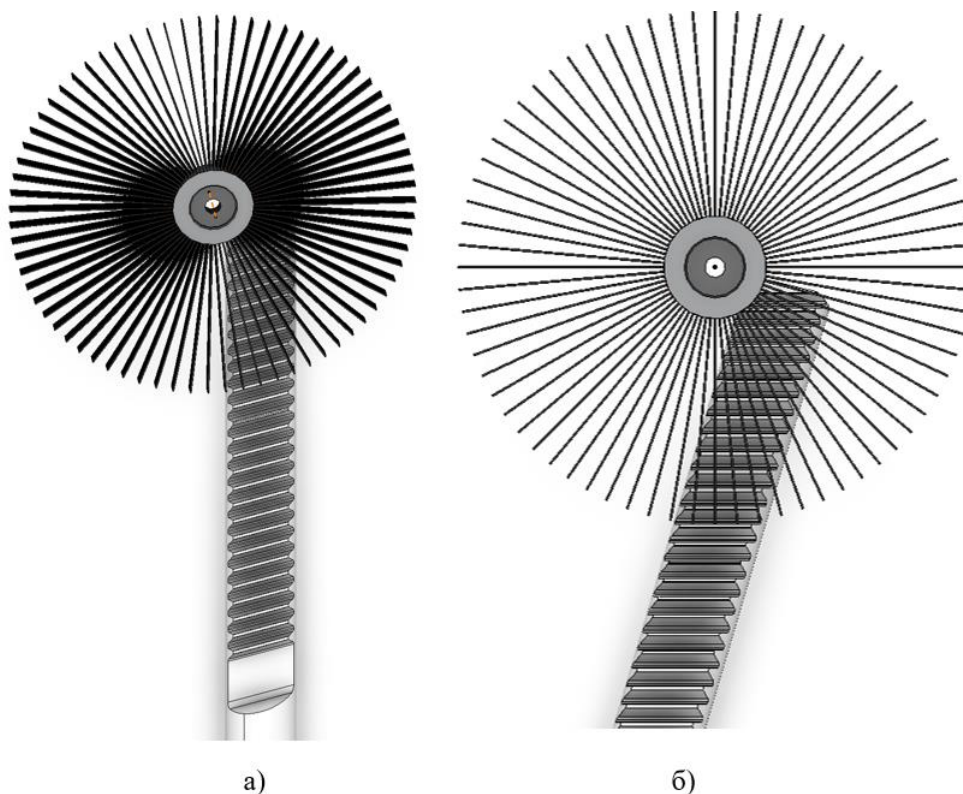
Обработка рулевой рейки гибким инструментом: а – вид сверху; б – вид нормалью к инструменту
